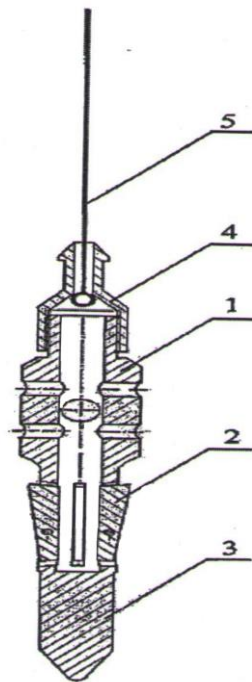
Ловитель забойного штуцера: 1 - Корпус ловителя; 2 - Захватные кулачки смещенного центра тяжести; 3 - Направляющий толкатель; 4 - Головка ловителя; 5 - скребковая проволока глубиномера
